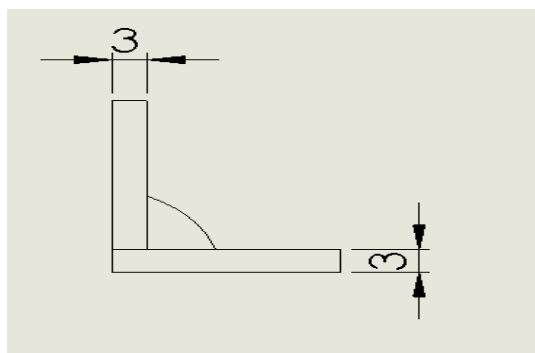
Diseño de junta soldada para placas de 3mm. Fuente: Jonathan Abril Investigador.
